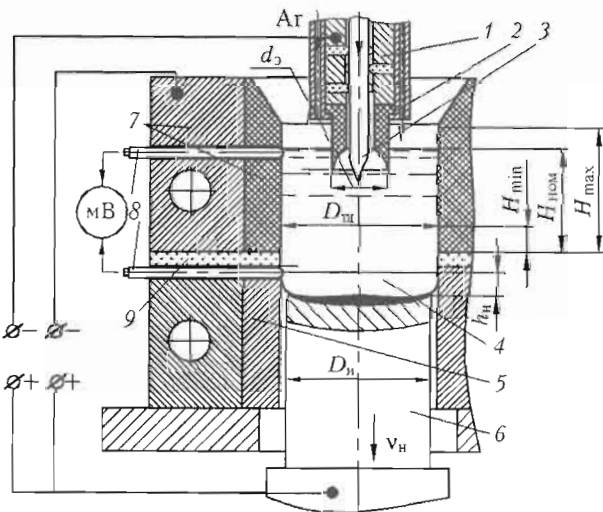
Схема электрошлаковой наплавки в ТПК: 1 — токоподвод к полюсу электроду; 2 — полый графитовый электрод; 3 — композиционная проволока; 4 — шлаковая ванна; 5 — сменная формирующая секция; 6 — торец наплавляемого изделия; 7 — изолятор; 8 — датчики для контроля уровней шлаковой и металлической ванны; 9 — разъемные графитовая и медная токоподводящие секции;  $v_n$  — скорость наплавки; остальные обозначения см. в тексте
